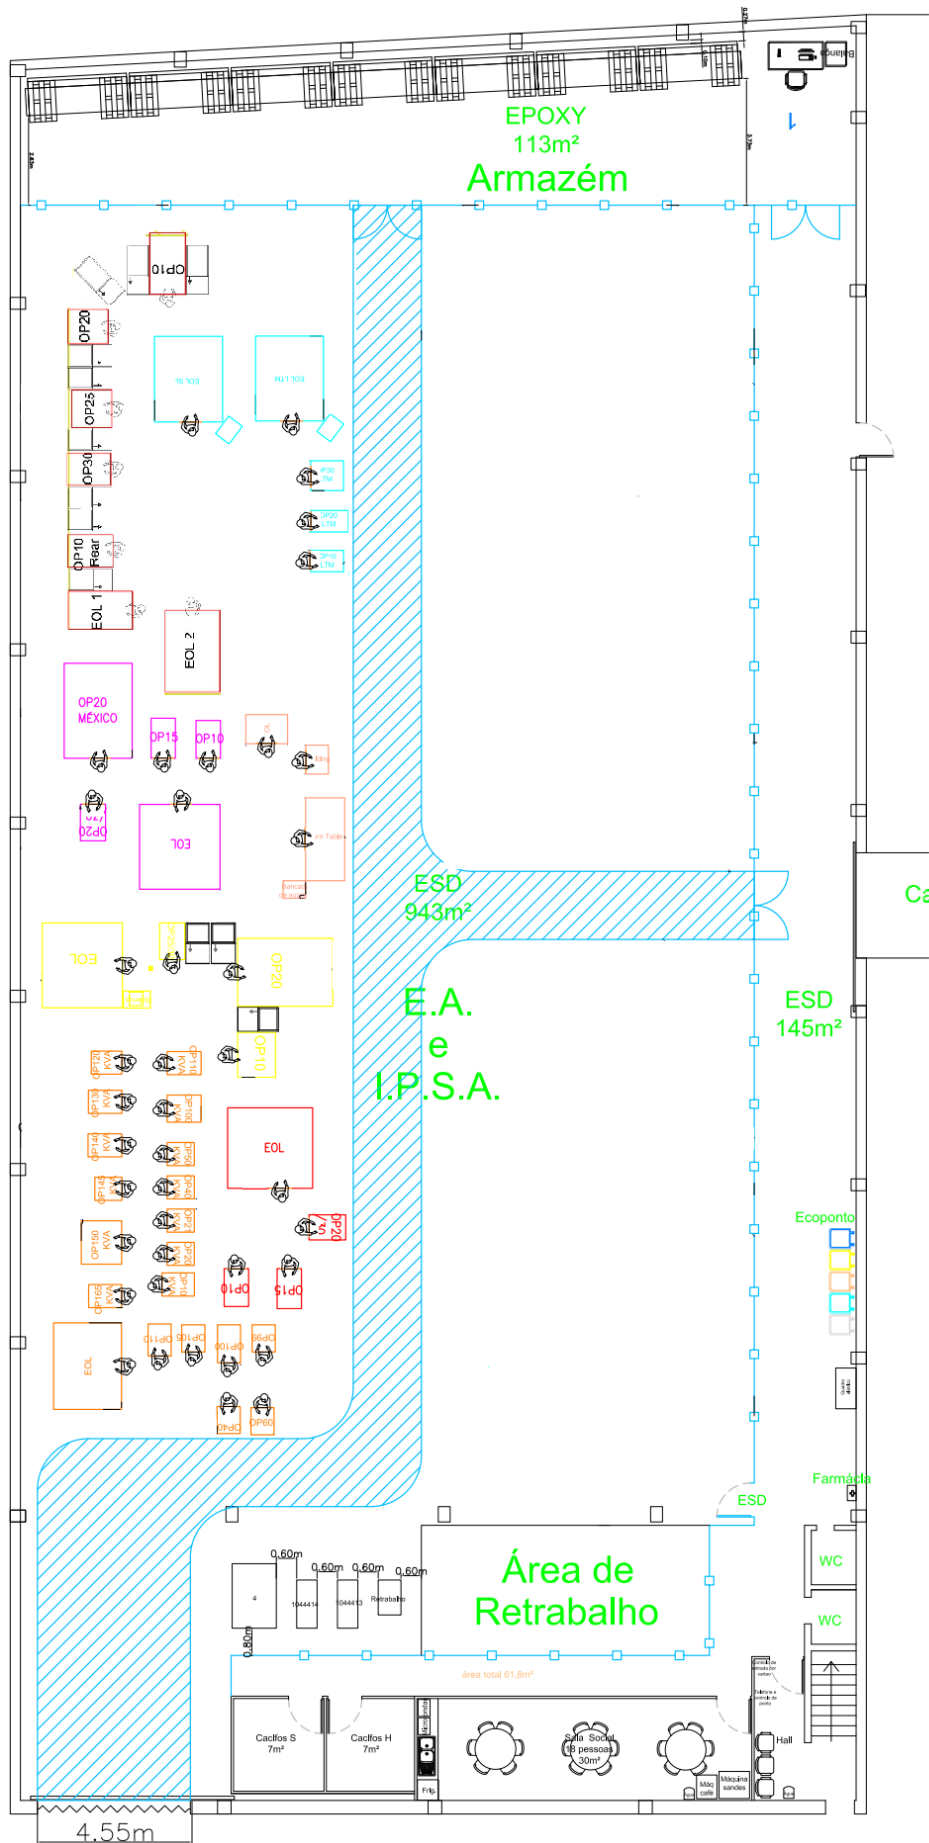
Layout proposto para o piso inferior do departamento de pré-séries
